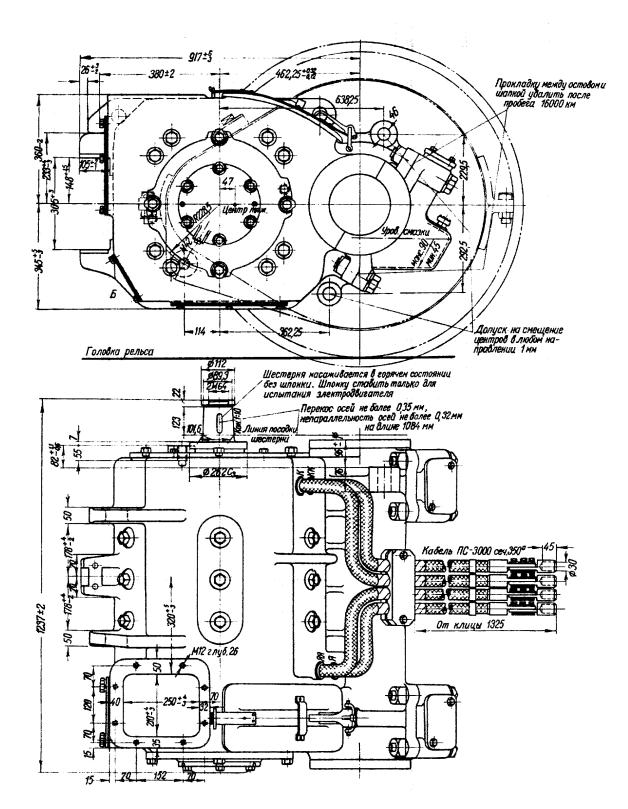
Габаритный чертеж электродвигателя ДК - 304.
